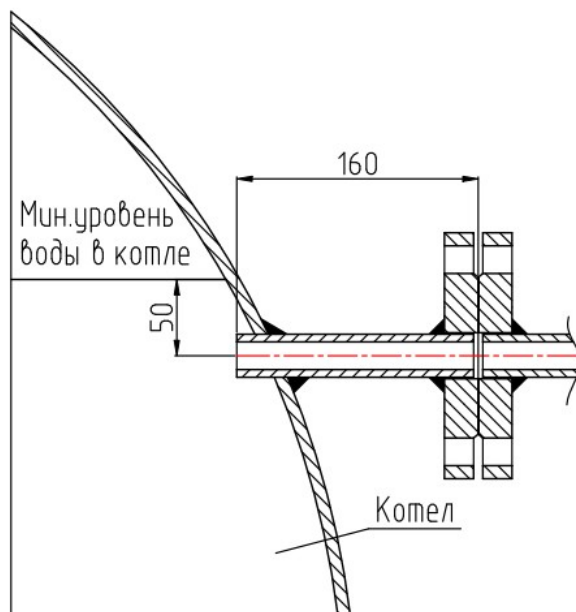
Схема приварки патрубка верхней продувки к корпусу котла.
